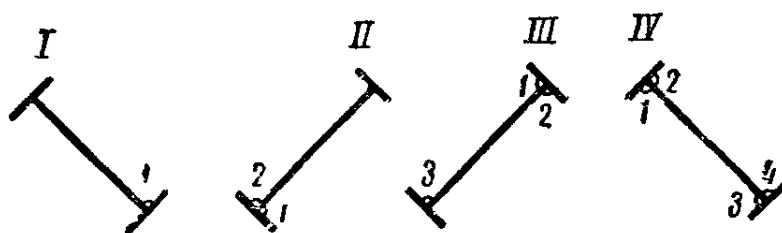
Схема последовательных положений (I, II, III и IV) балки при сварке поясных швов
